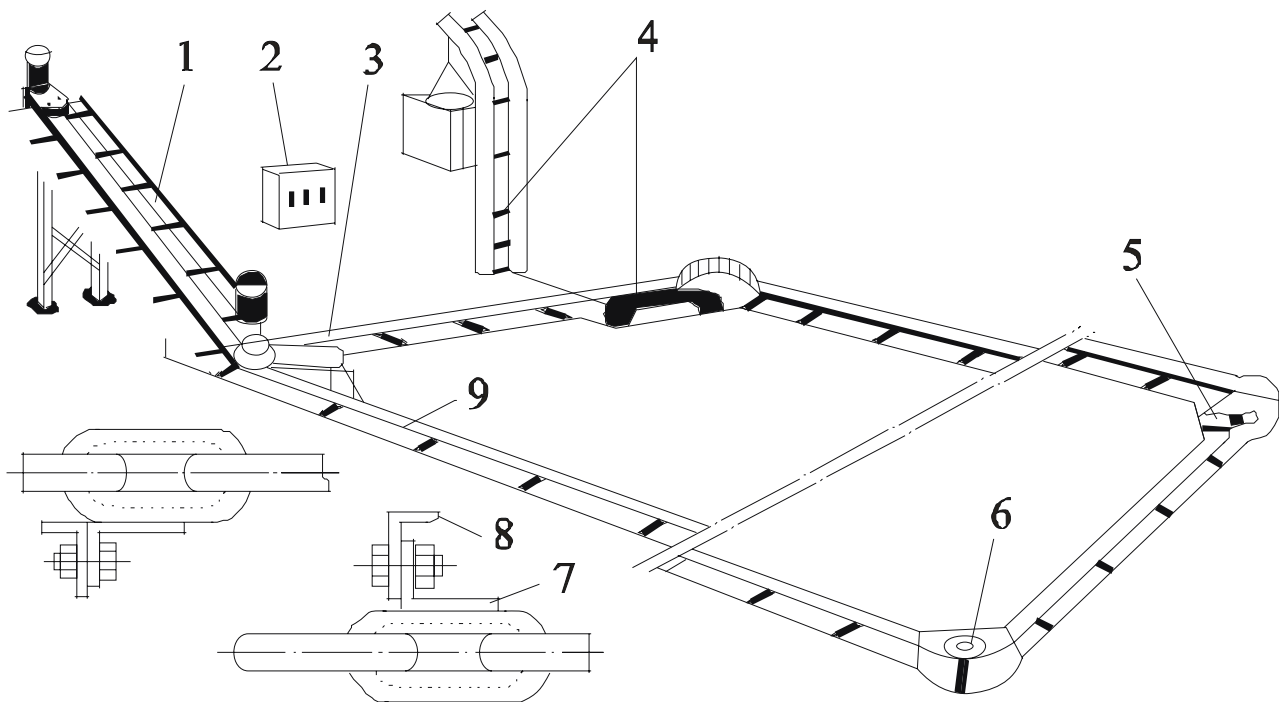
Транспортер скребковый навозоуборочный ТСН-160А:
